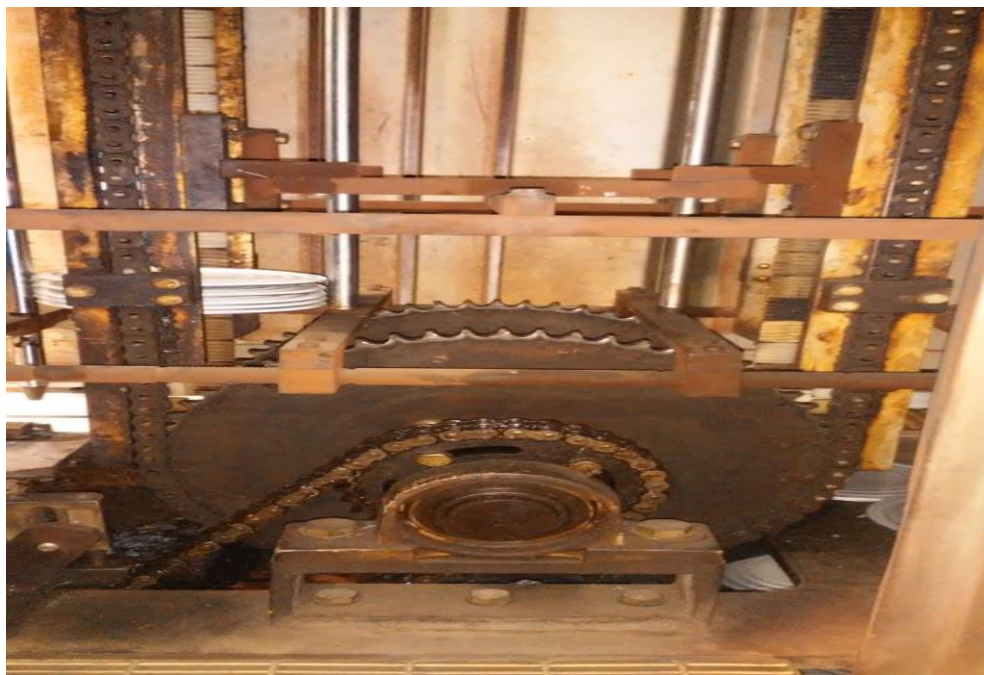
Máquina de horneado de la empresa Metalpren s.a
